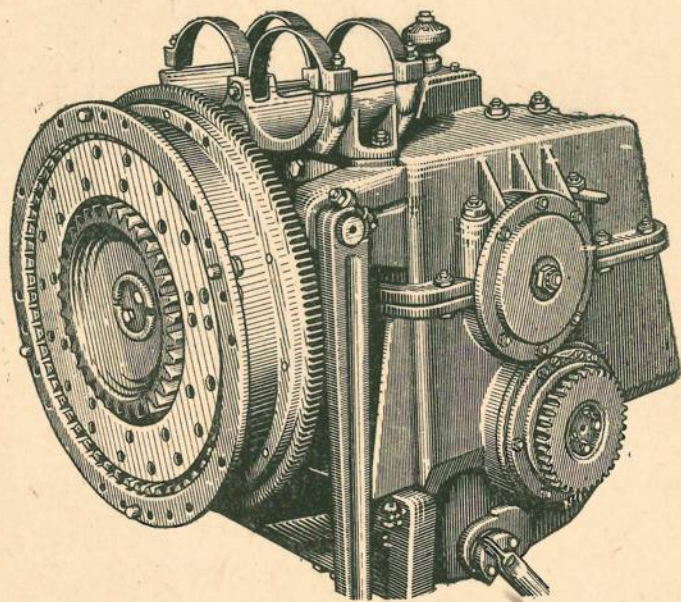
Коробка перемены передач с главным фрикционом перед установкой в корпус танка
